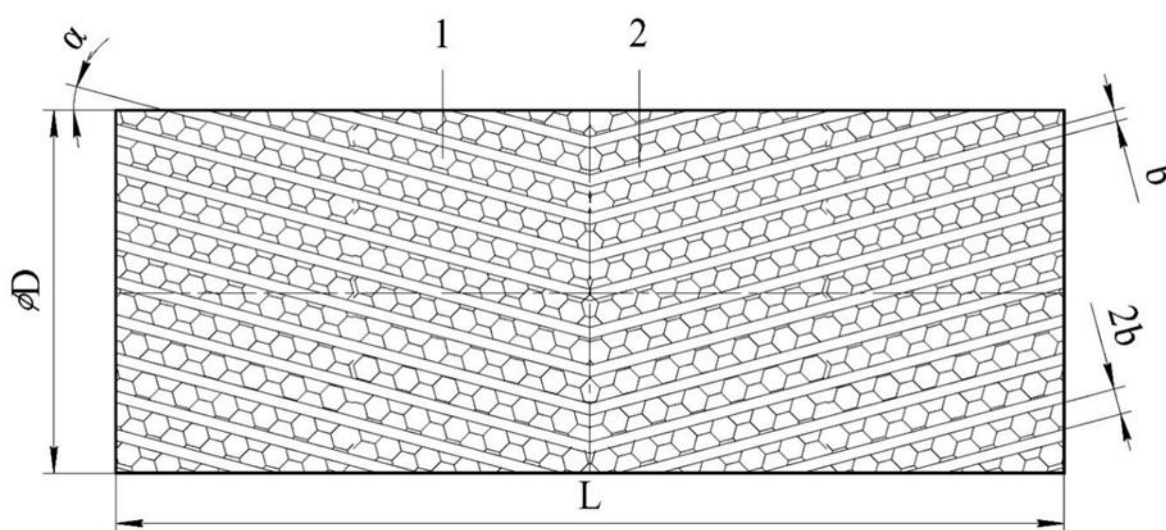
Зміцнювальна обробка циліндричної поверхні притискного валу механізму координатного транспортування, 1 – постійний регулярний мікрорельєф; 2 – частково регулярний мікрорельєф; b – ширина плоскопаралельних заглибин; $2b$ – відстань між заглибинами; α – кут нахилу заглибин; $\varnothing D$ – діаметр роликів; L – ширина роликів.
